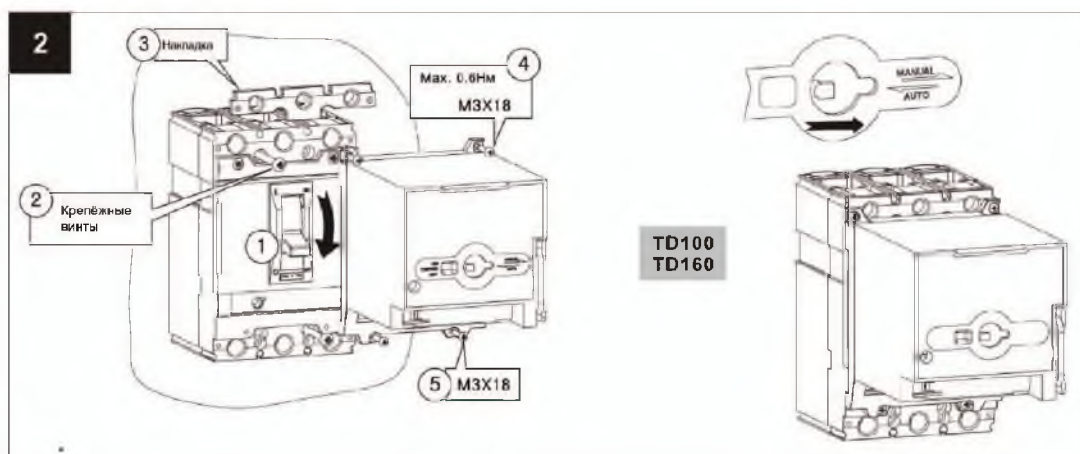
Установка моторного привода на выключатели TD100 и TD160
